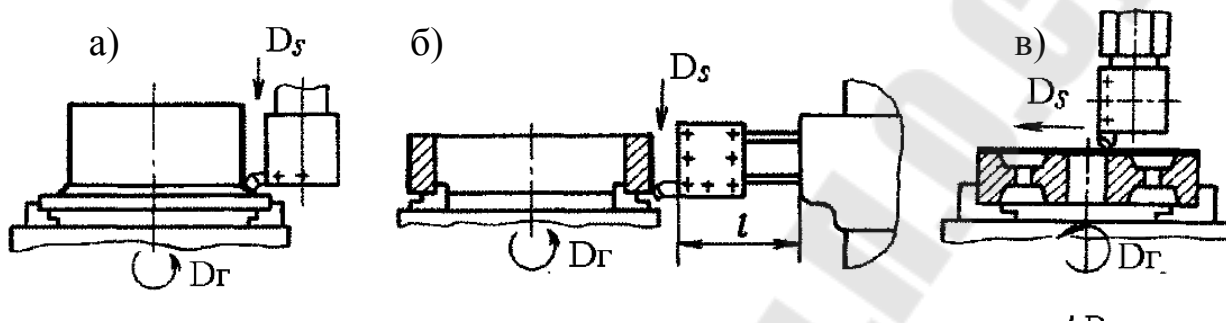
Схемы обработки на токарно-карусельном станке
